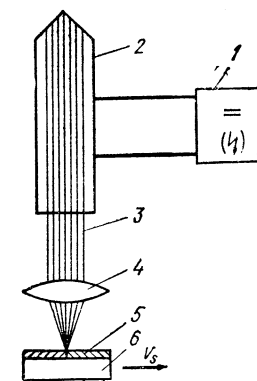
Принцип сварки: 1 — источник питания; 2 — лазер; 3 — лазерный луч; 4 — лазерная оптика; 5 — изделие; 6 — манипулятор (устройство для перемещения свариваемого изделия)
